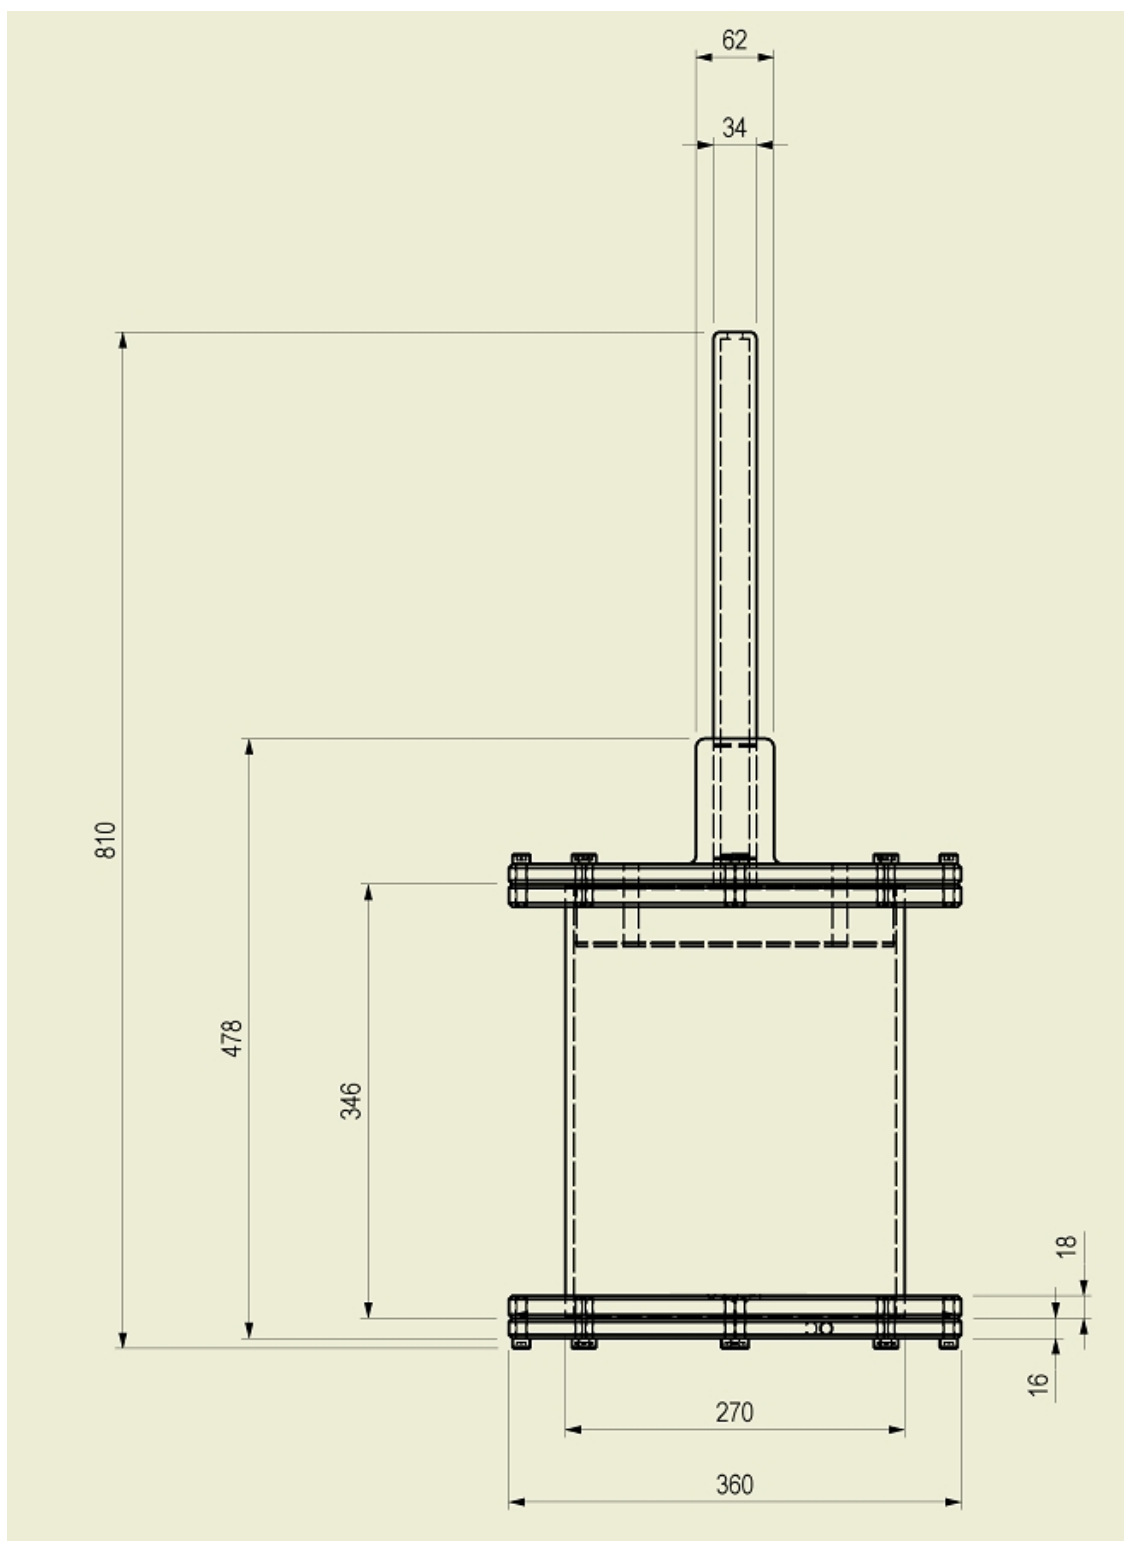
Corte do consolidômetro. Todas as dimensões do equipamento em mm.
